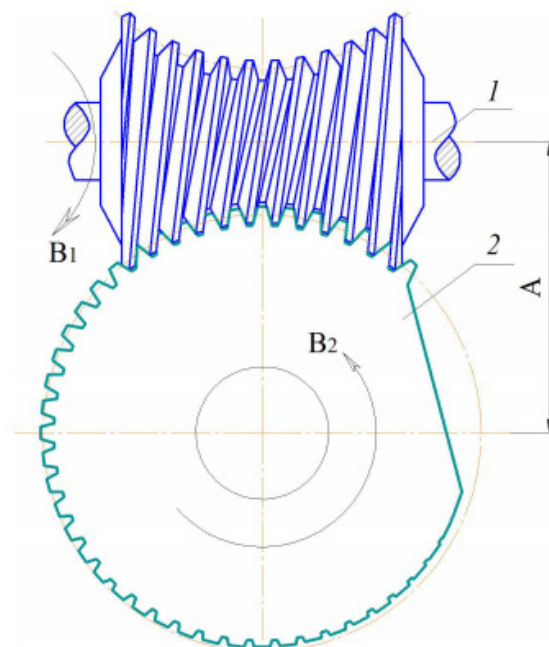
Схема багаторізцевої головки для нарізування ВП глобоїдного черв'яка по методу кругового протягування: 1 - заготовка глобоїдної черв'яка; 2 - інструмент; А - міжосьова відстань; B_1 - обертання заготовки глобоїдної черв'яка; B_2 - обертання інструменту
